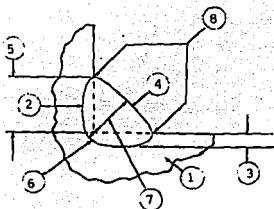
Detalles de la soldadura de filete.
